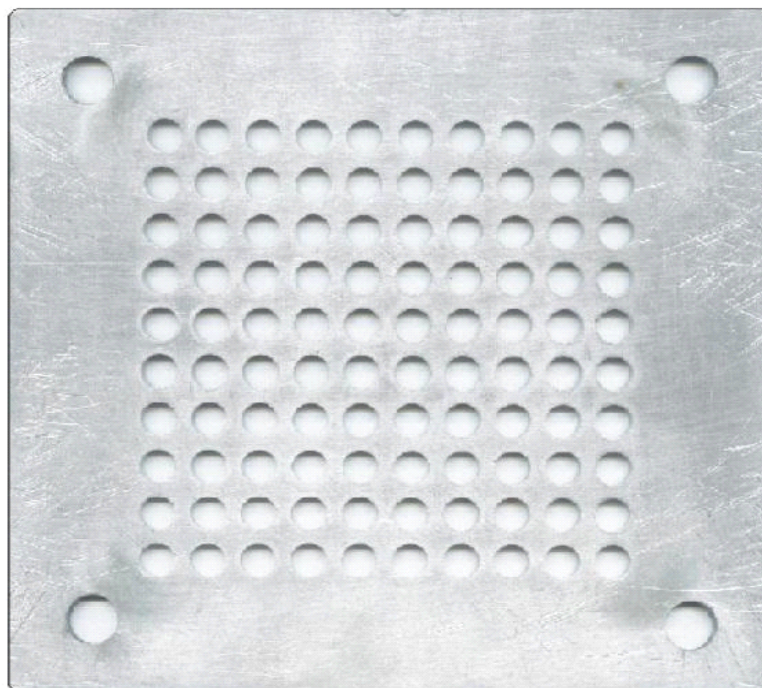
Placa de alumínio usada como suporte de fixação sobre a mesa da máquina.
